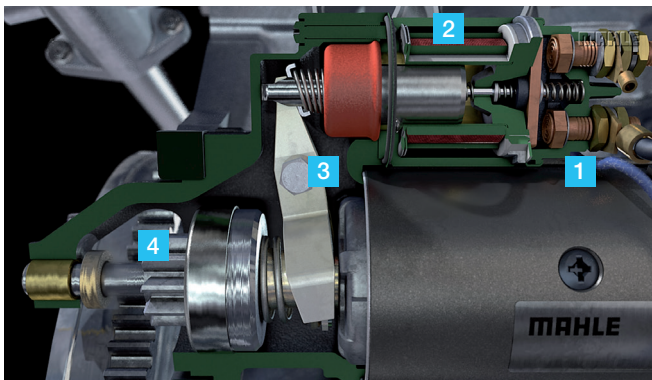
Starter im Schnitt mit Kontaktbrücke (1), Magnetschalter (2), Einrückhebel (3) und Ritzel mit Freilaufkupplung (4)
